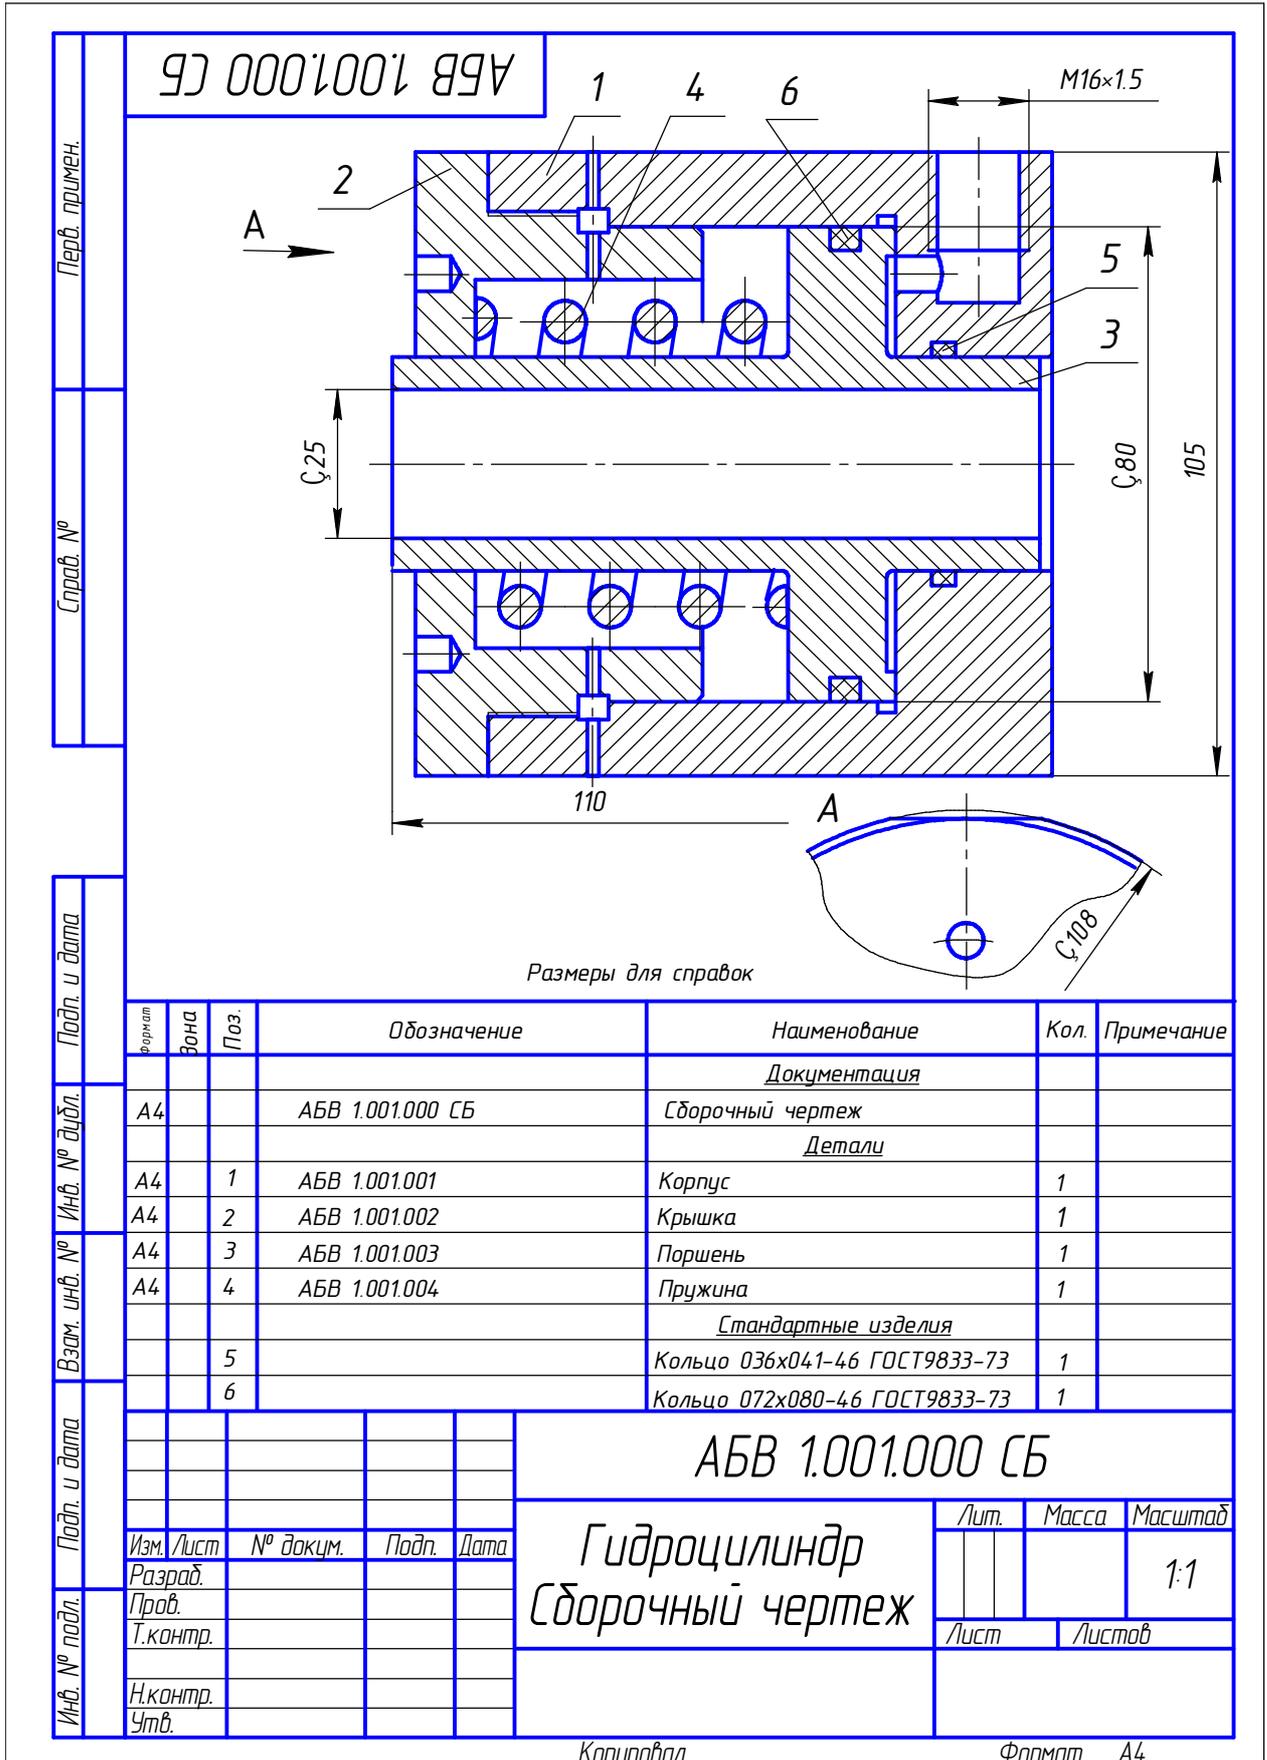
Сборочный чертёж изделия «Гидроцилиндр»
